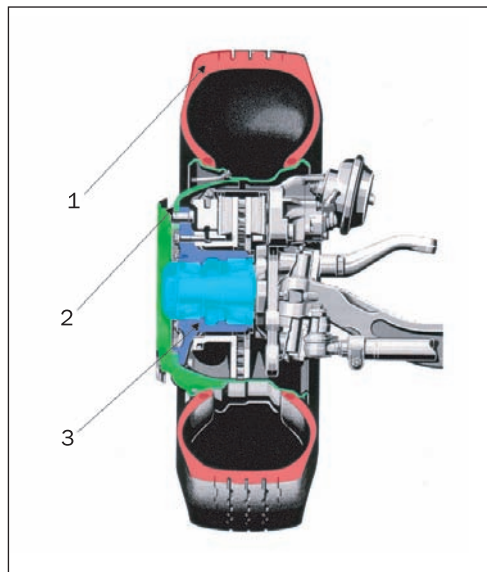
Устройство автомобильного колеса: 1 — шина; 2 — обод колеса; 3 — ступица
